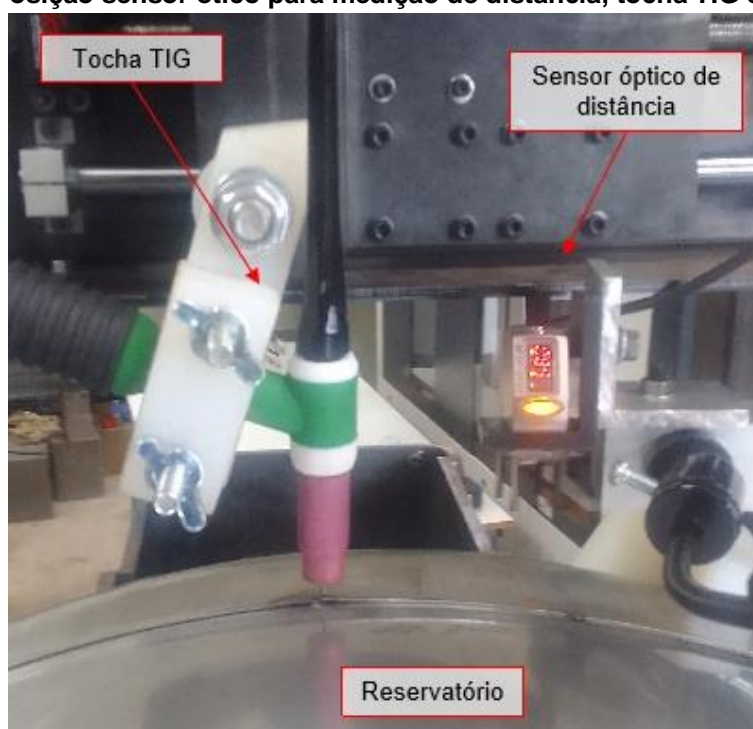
Foto do protótipo de máquina de solda circunferencial automatizado do projeto SOLIS / EMBRAPII / UFSCar.
